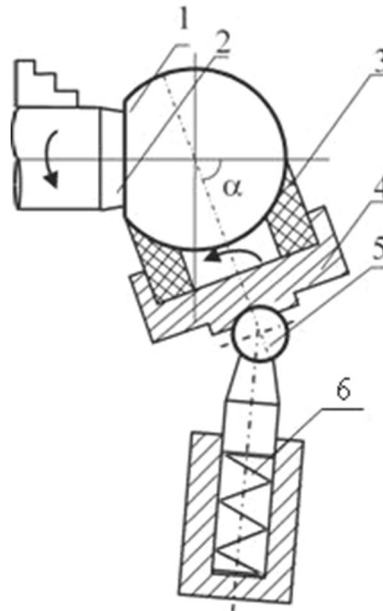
Технологічна схема вільного притирання: 1 – деталь; 2 – оправка; 3 – притир; 4 – обойма; 5 – шарнір; 6 – пружна державка
